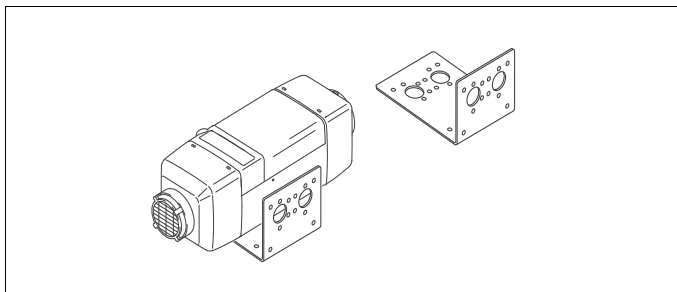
Fissaggio di Air Top mediante staffa di supporto
